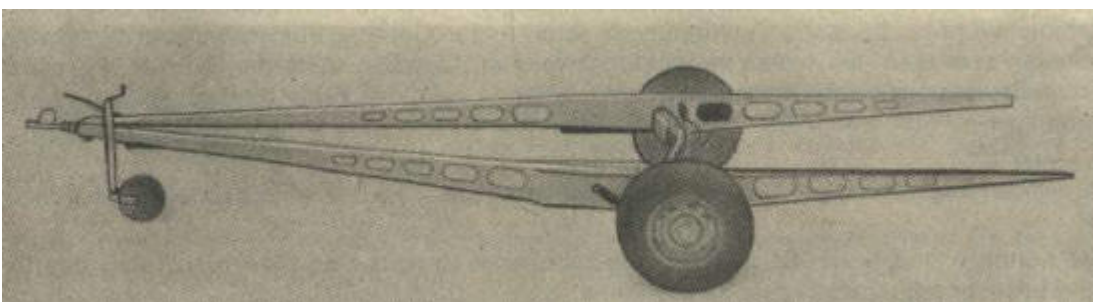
Kober-Fahrwerk mit Schräglengerachse und in der neutralen Profidfaser eingebrachten Aussparungen zur Masseerleichterung
